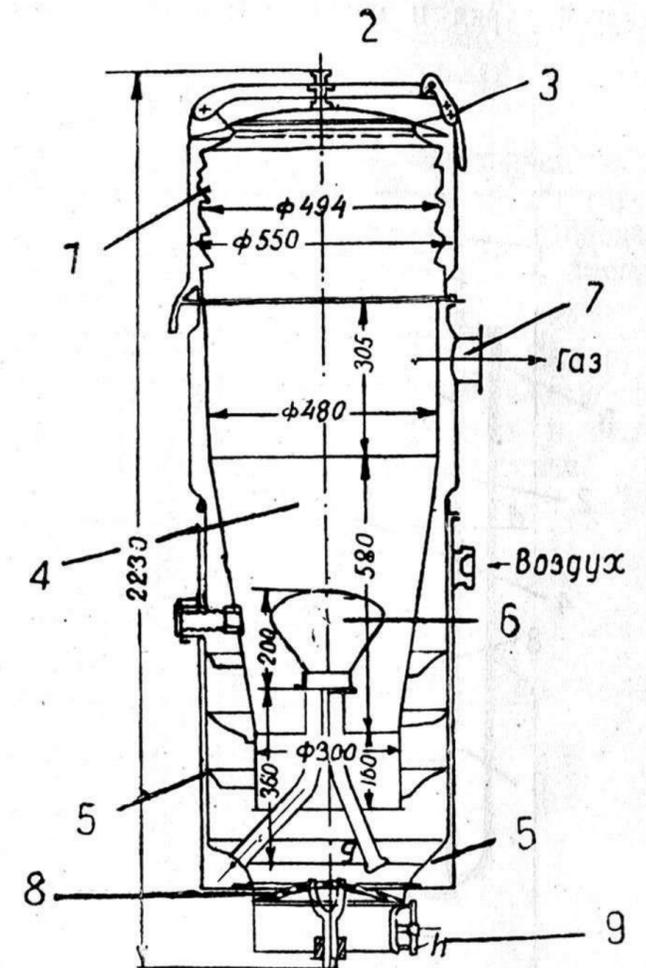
Газогенератор Кромаг-Сагам тип С-3, № 100. 1—бункер с отверстием для прохода паров воды; 2—скоба загрузочного люка; 3—накидной рычаг (замок); 4—топливник; 5—воздухоподводящий канал; 6—шипообразное сопло; 7—штуцер для отсоса газа; 8—качающийся колосник; 9—зольниковый люк
